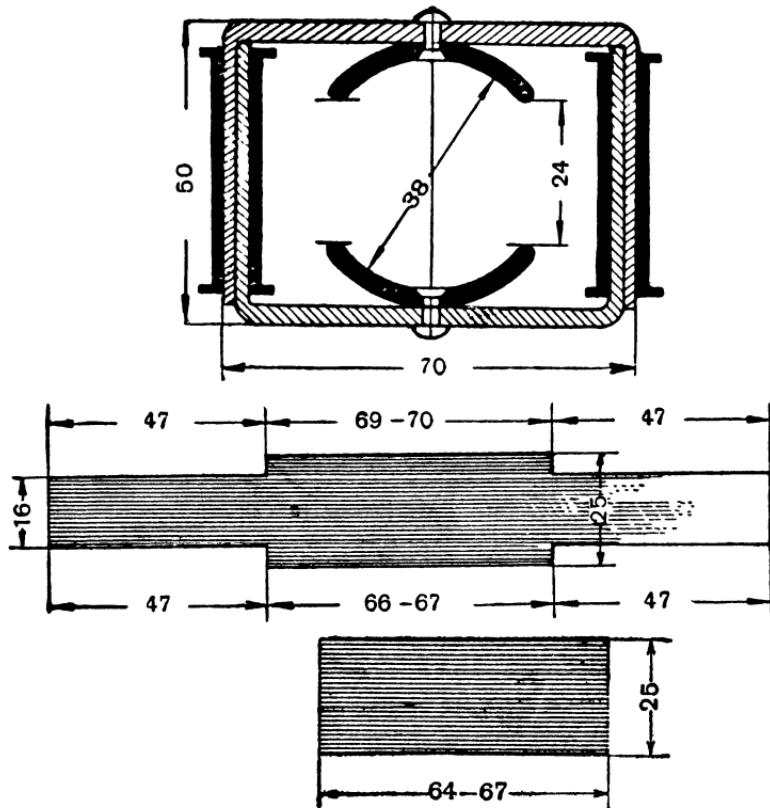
Детали статора № 5 (рис. 23). Наверху — схема сборки; в середине — заготовка для скобы. Верхние размеры — для верхней скобы, нижние — для нижней. Внизу — заготовка для башмака.
